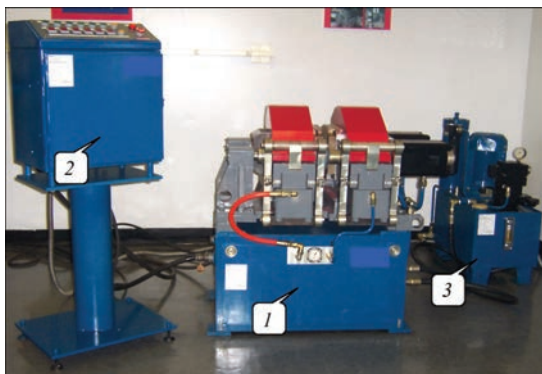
Установка МД103: 1 — сварочная машина; 2 — шкаф управления; 3 — насосная станция
